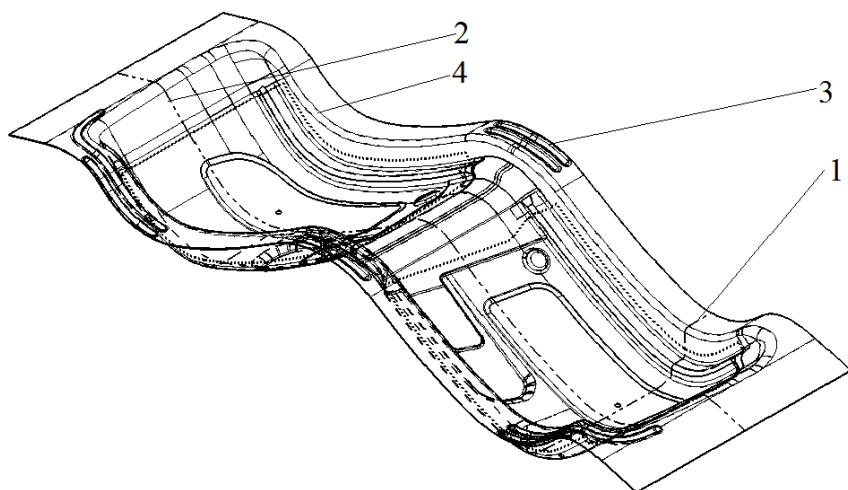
Аксонометрия заготовки для детали «Бампер»:
